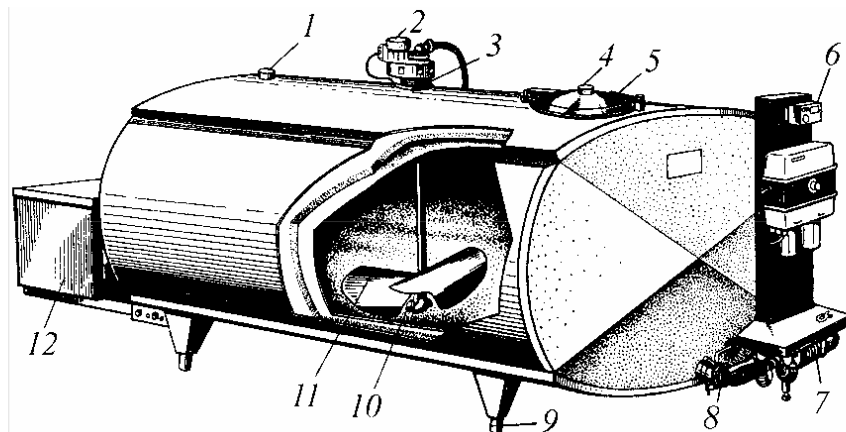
Танк охолоджувач закритого типу фірми "Alfa-Laval" (Швеція): 1, 4 – горловини для заливання молока; 2 – двигун мішалки; 3 – вентиляційний отвір; 5 – кришка; 6 – блок керування; 7 – насос для подачі мийного розчину; 8 – зливний клапан; 9 – опори, регульовані за висотою; 10 – пристрій для миття резервуара; 11 – мішалка; 12 – холодильний агрегат [19].
